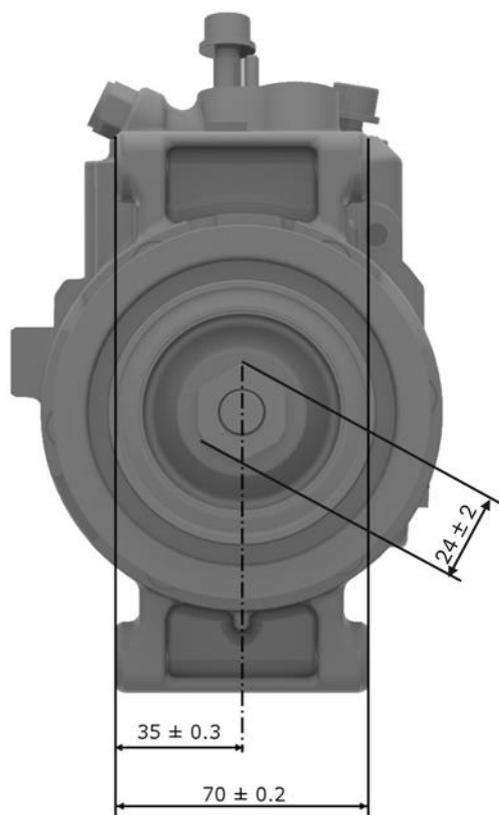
Размеры компрессора климатической установки (вид спереди).
